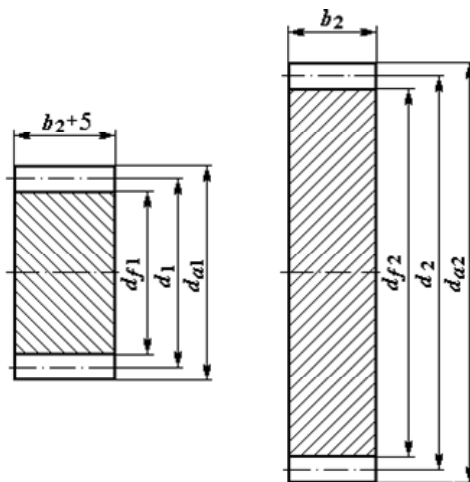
Эскизы шестерни (1) и зубчатого колеса (2)
